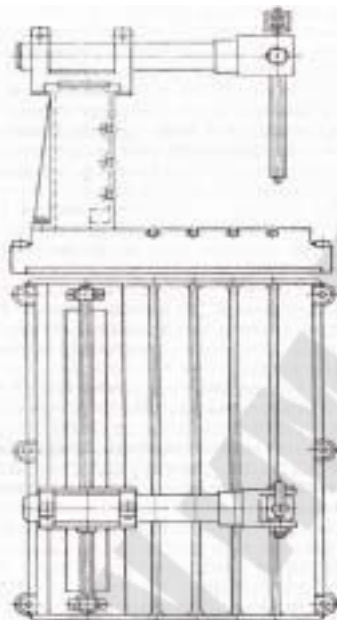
Универсальный стенд для испытания на жесткость
